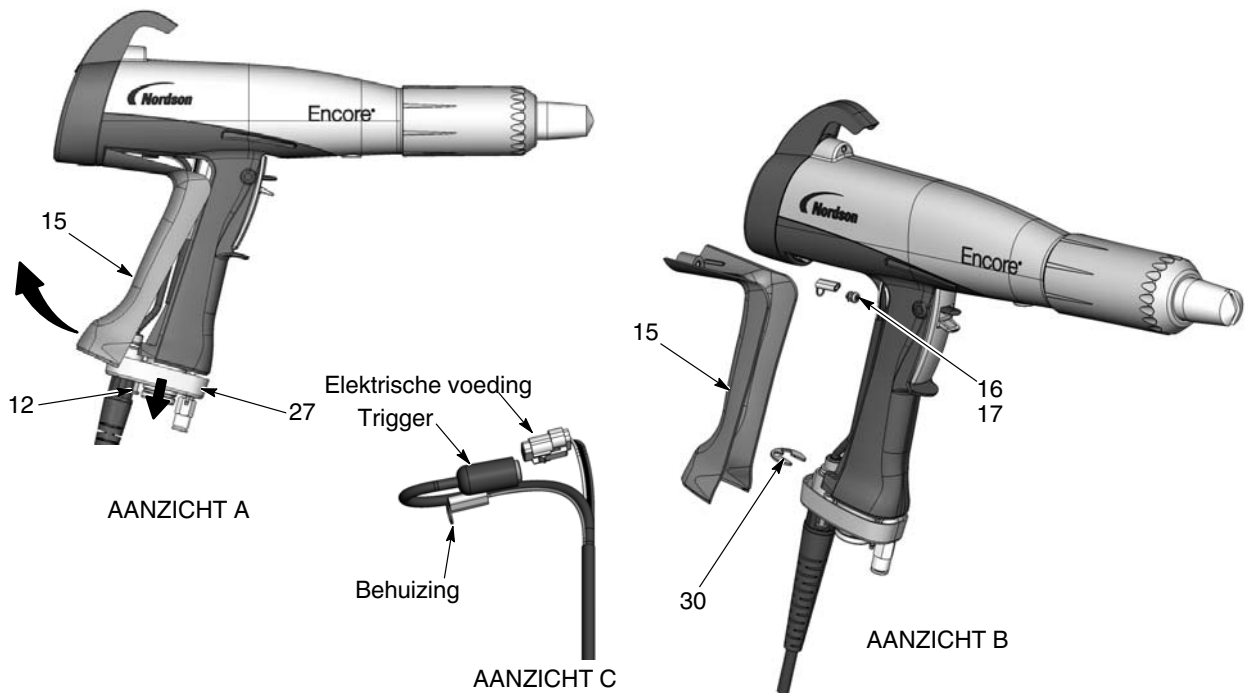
Pistoolhuis installeren aan de pistoolgreep
